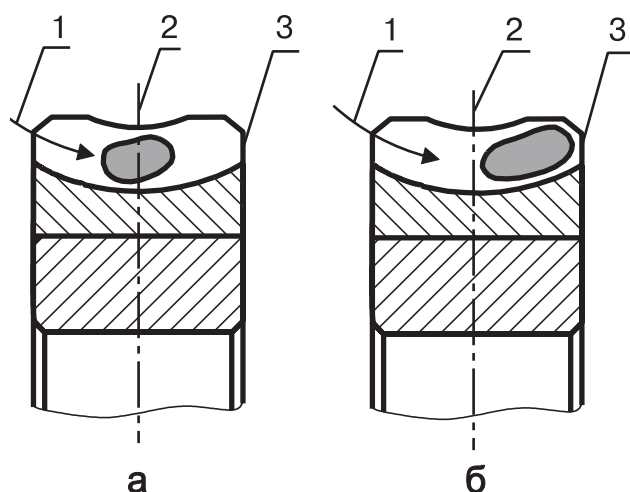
Варианты расположения начального пятна контакта на боковой поверхности зубьев червячного колеса (для правого направления витков червяка):
